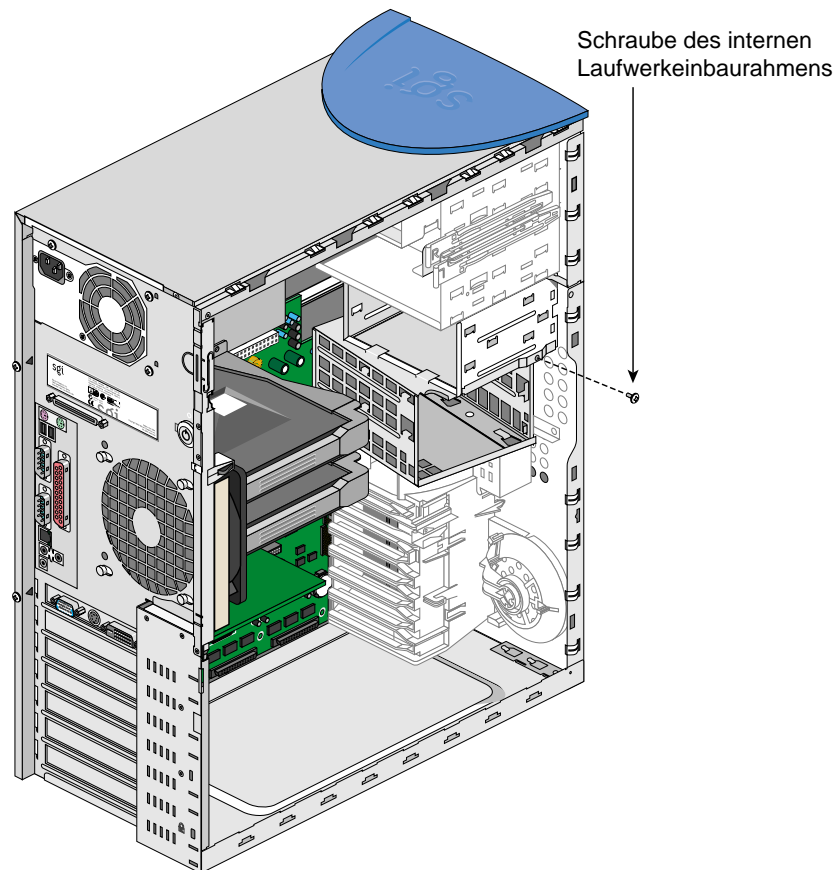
Lage der Schraube des internen Laufwerkeinbaurahmens
